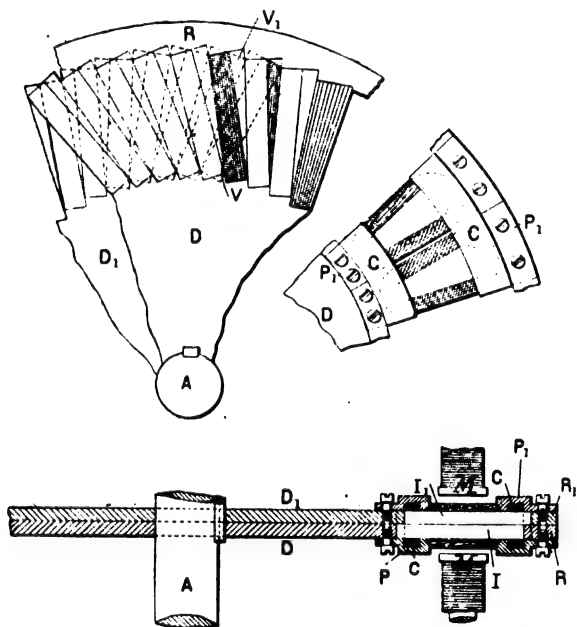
, 2 et 3. — Machine à disque et à fer dispositif de Siemens frères et Lauckert.
